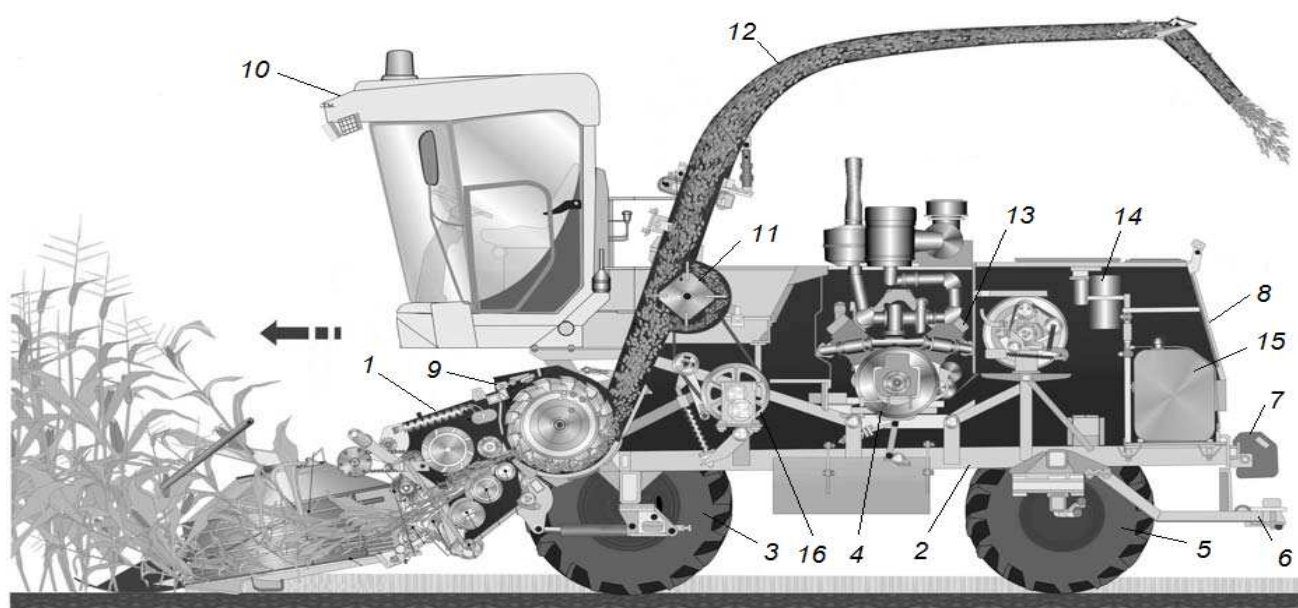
Самоходный измельчитель: 1- питающий аппарат; 2-рама; 3-ведущее колесо; 4-главный контрпривод; 5-управляемое колесо; 6-прицепное устройство; 7-противовес; 8-капот; 9-измельчающий аппарат; 10-кабина; 11-конфузор с ускорителем; 12- силосопровод; 13-моторно-силосовая установка; 14-масляный бак; 15-топливный бак; 16-редуктор ускорителя
